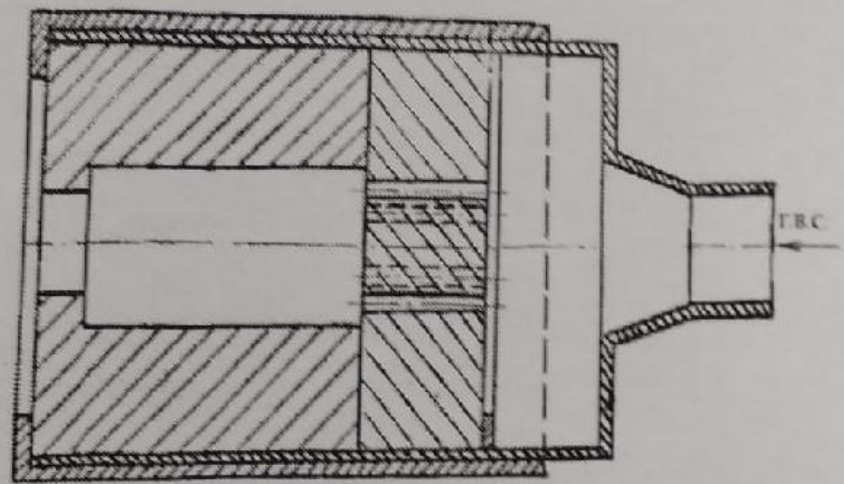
Горелка местного скоростного нагрева для нагрева длинных изделий
